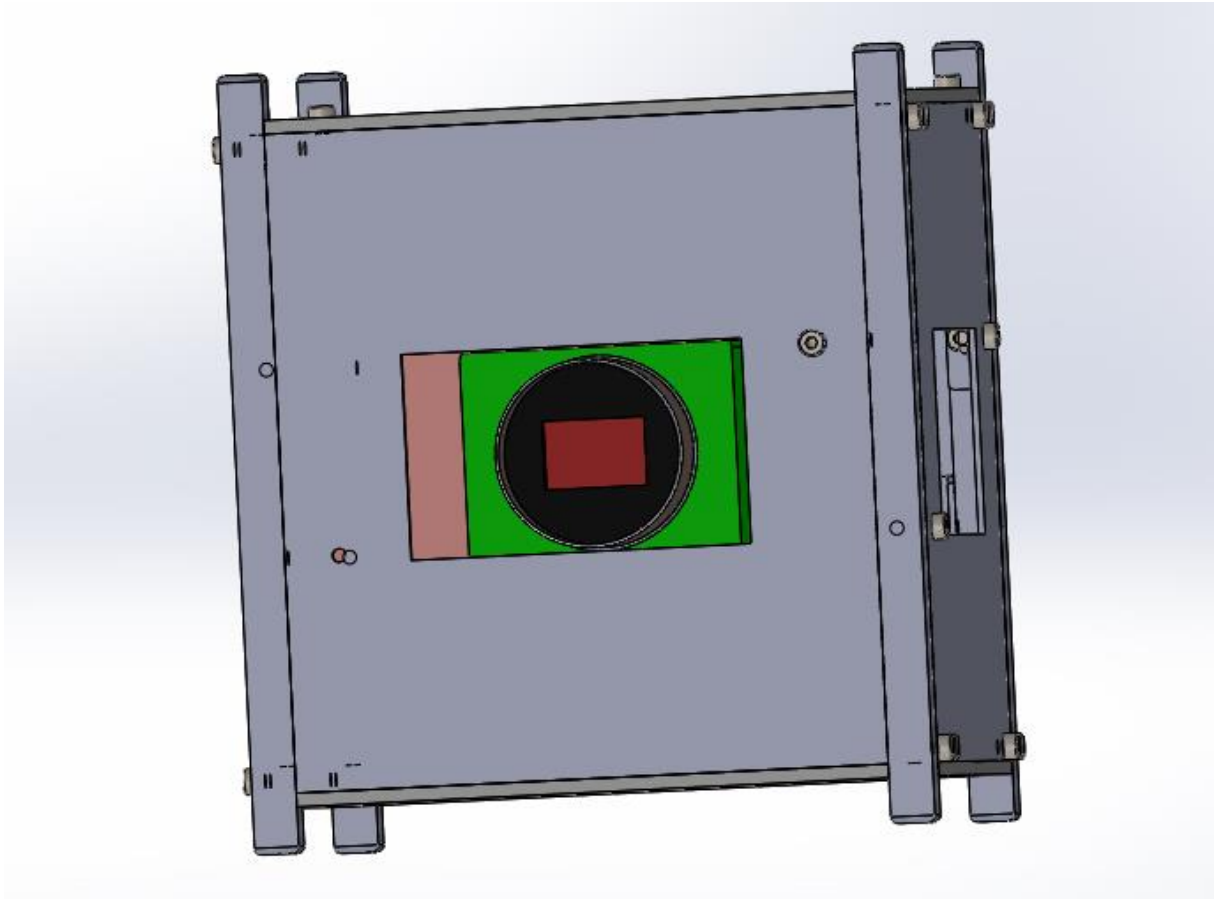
Sugestão de *assembly*. Detalhe *payload
